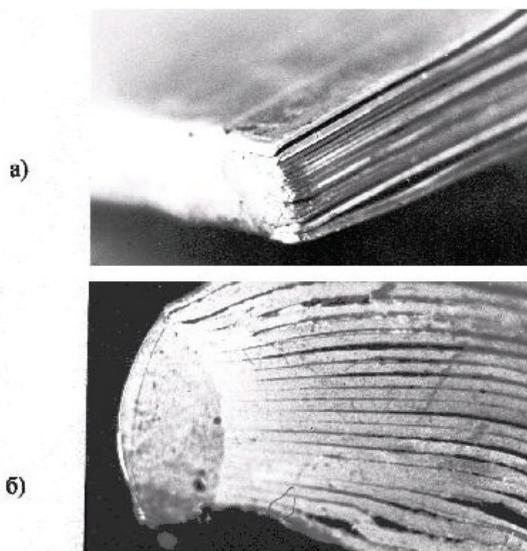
Наплавка трехфазной дугой торца пакета шинпровода из тонколистового алюминиевого сплава:
